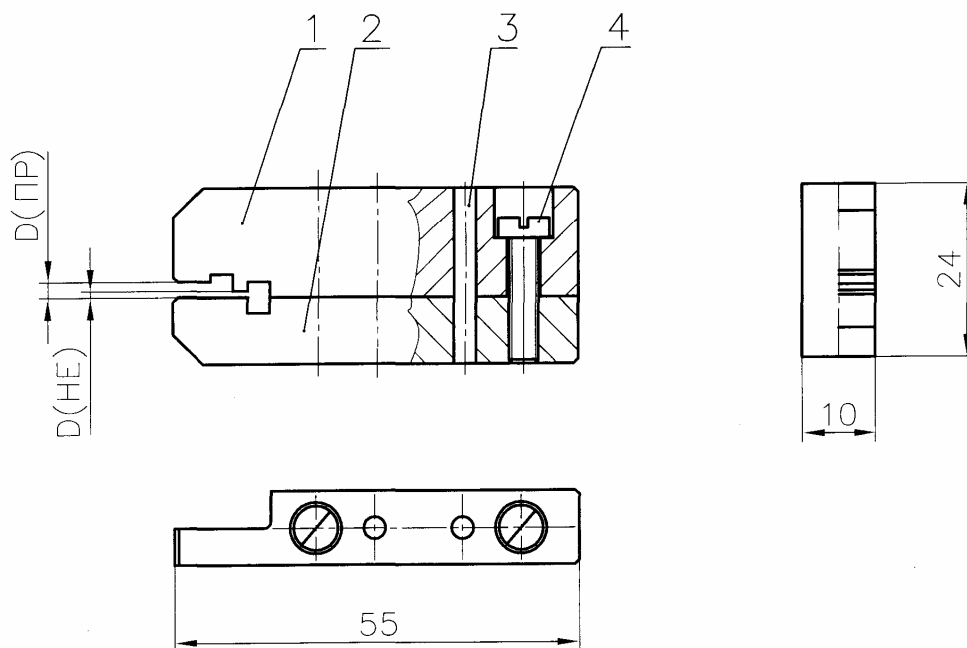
Калибр-скоба односторонний двупредельный:
